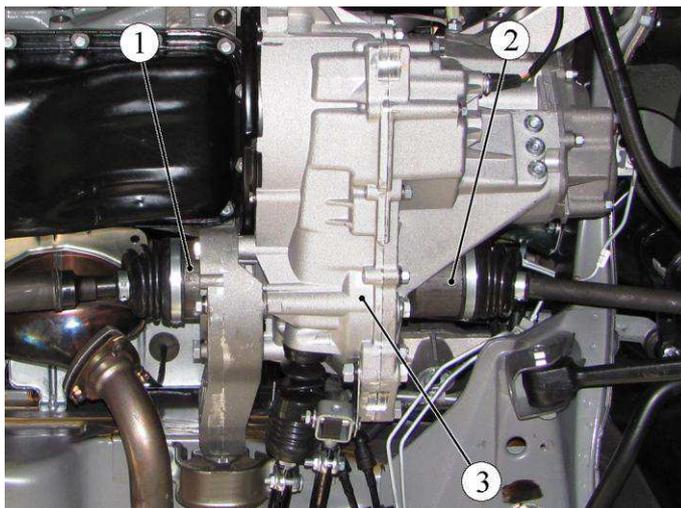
Отсоединение внутренних шарниров приводов от коробки передач:
